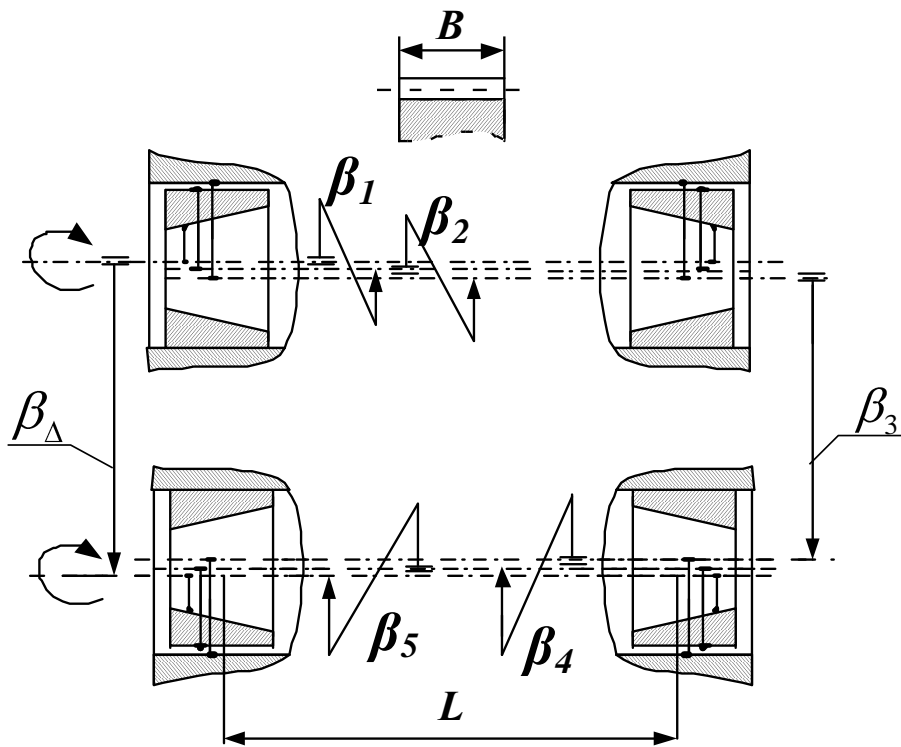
Схема размерной цепи, описывающей формирование параллельности рабочих осей зубчатой передачи
